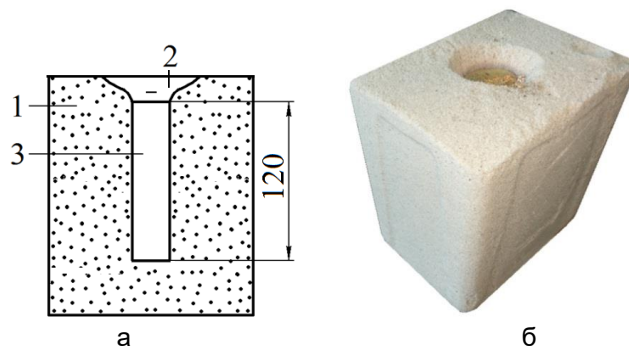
Схема ПРФ для виготовлення зразків циліндричної форми $\varnothing 30 \times 120$ мм (а) та загальний вигляд залитої ПРФ (б): 1 – ливарна форма; 2 – ливникова воронка; 3 – робоча порожнина ПРФ
